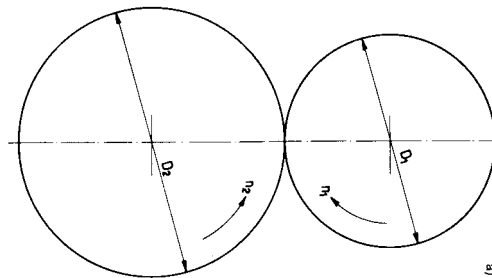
Modelo cinemático para a engrenagem [Manfé]
